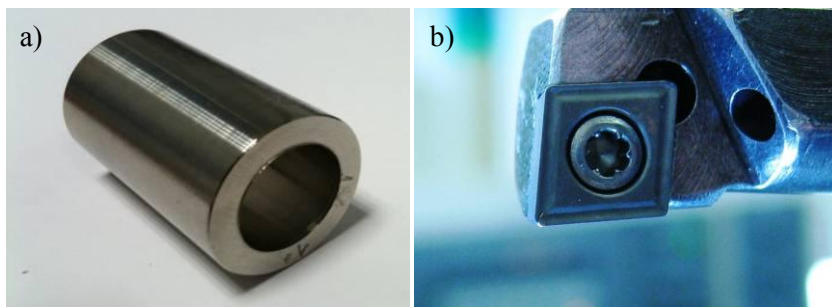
(a) Pièce d'essai de tournage et (b) plaquette amovible CCMT 060204.
